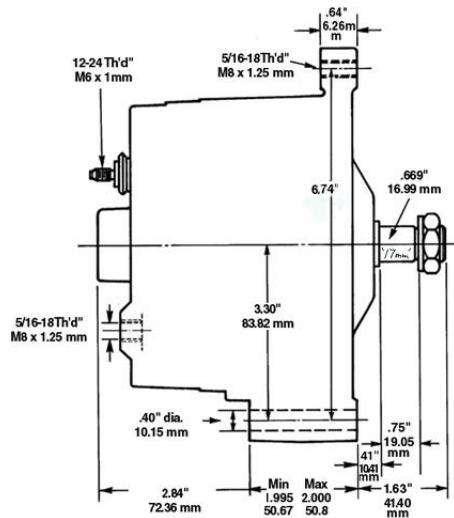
Vista y dimensiones principales del alternador modificado DC-520
